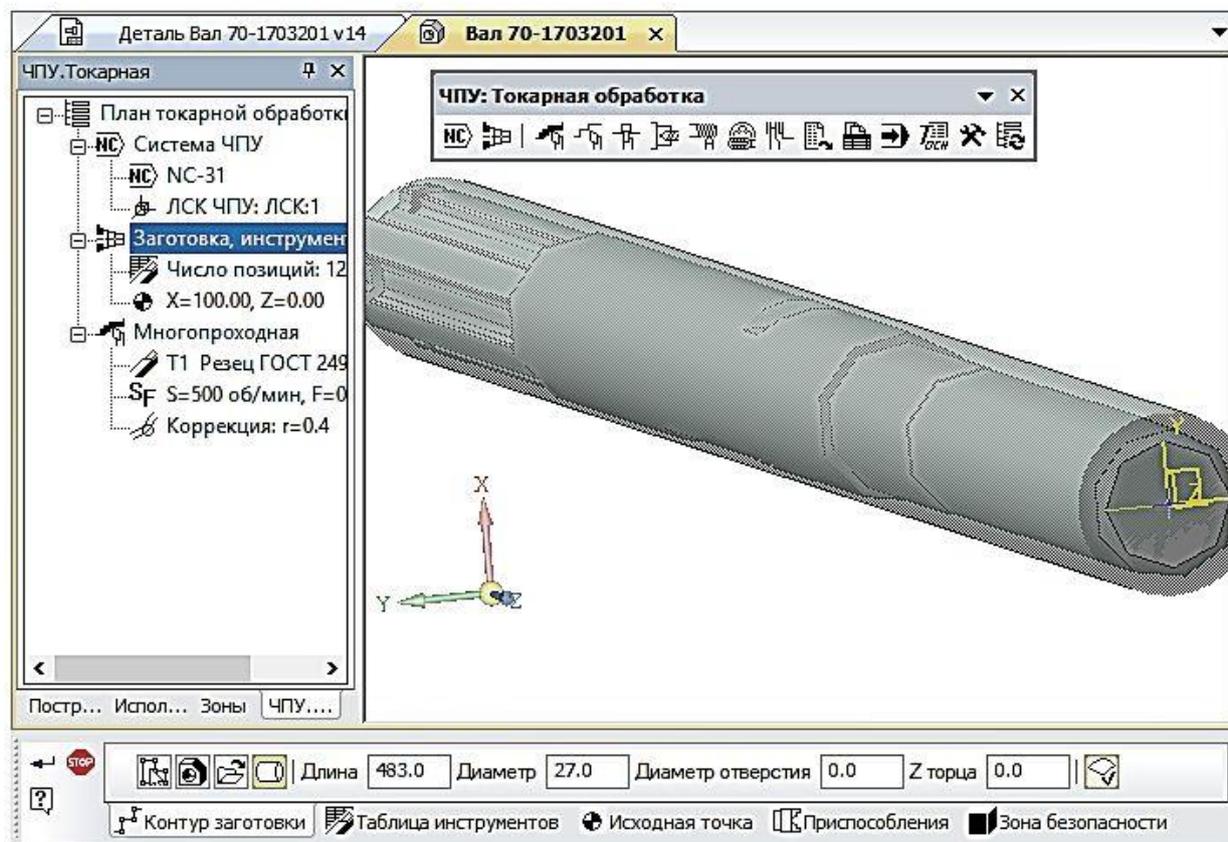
Определение заготовки, инструментов, приспособления, исходной точки и зоны безопасности
